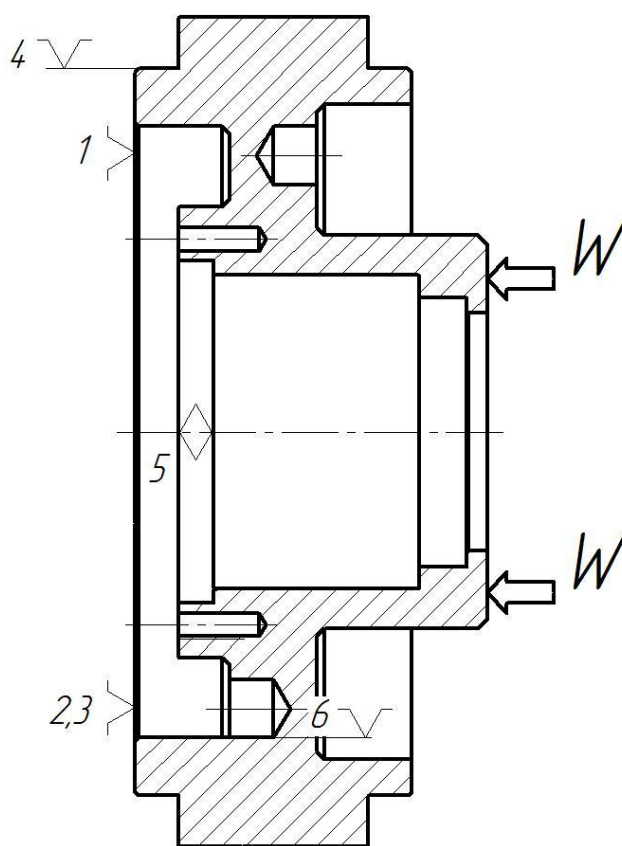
Принципиальная схема зажима заготовки в приспособлении с указанием мест приложения силы зажима.
